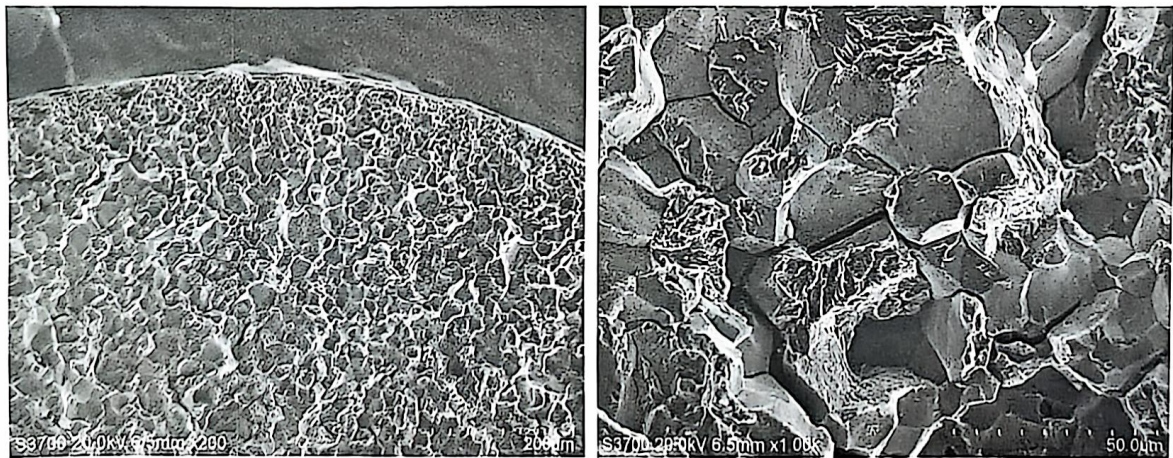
螺钉裂纹源附近断口的微观形貌
